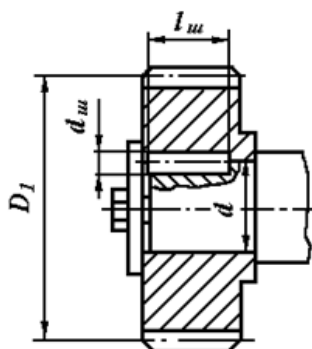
Шпоночное соединение зубчатого колеса с валом
